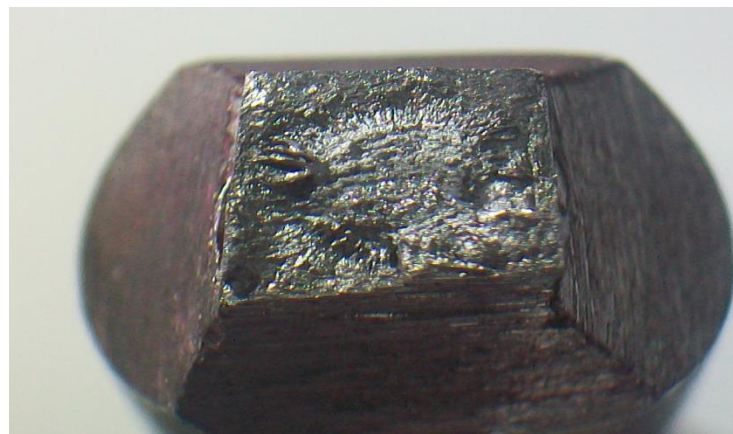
Sección transversal de la rotura de la probeta 4.
